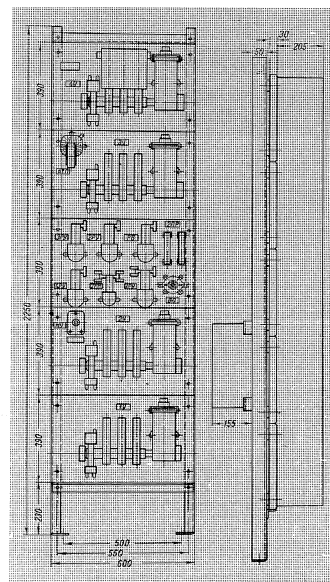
Габаритные размеры станции СУ2240-32. Вид спереди.
